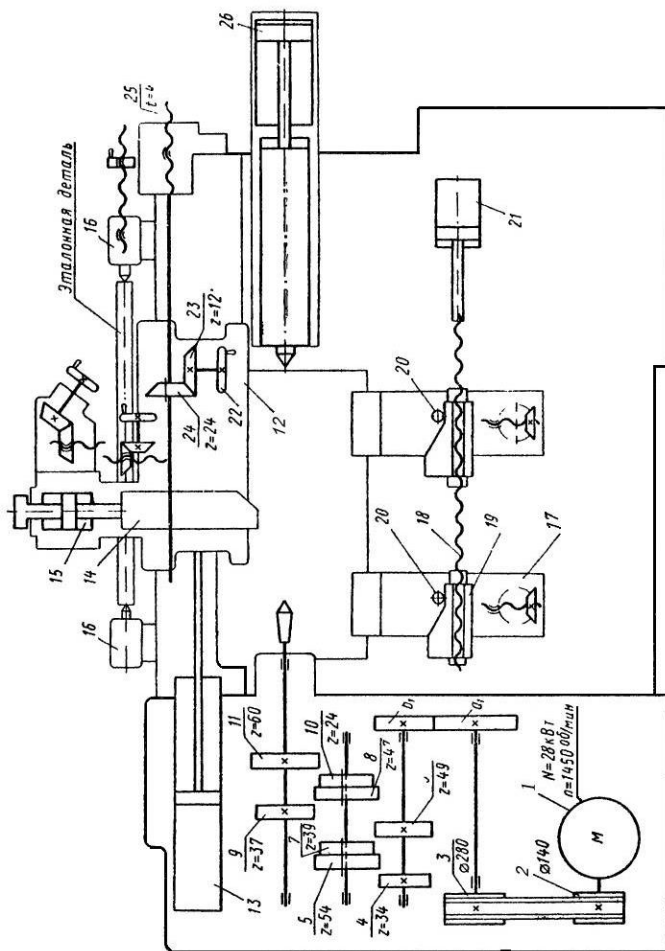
Кинематическая схема станка-полуавтомата 1722 [18]: 1 – электродвигатель; 2, 3 – ременная передача; 4-11 – четырехступенчатая коробка скоростей; 12 – копировальный суппорт (КС); 13 – гидроцилиндр продольной подачи КС; 14 – салазки КС; 15 – гидроцилиндр поперечного перемещения КС; 16 – зажимные центры; 17 – подрезной суппорт; 18 – резцовая тяга; 19 – копир; 20 – пальцы; 21 – гидроцилиндр поперечной подачи; 22 – маховик; 23, 24 – коническая передача наладки КС
